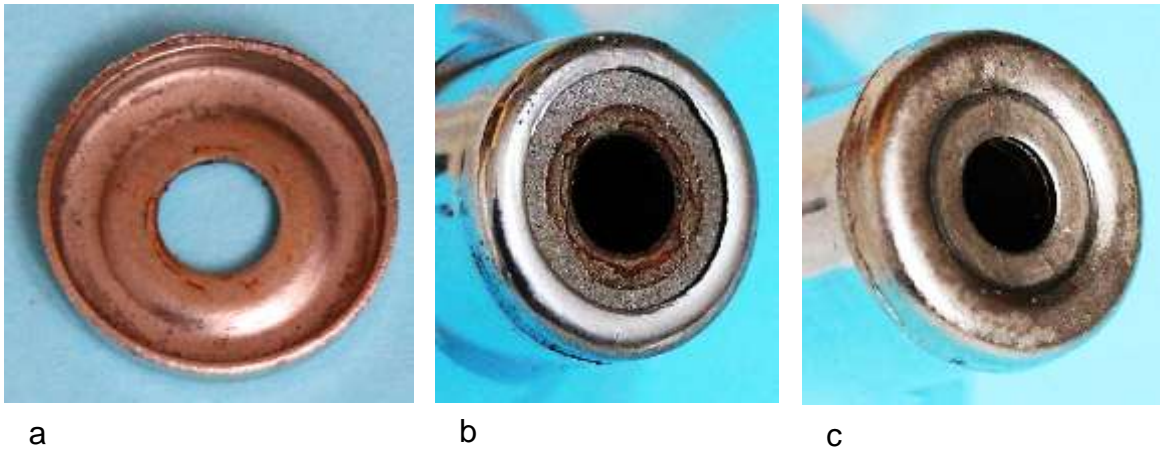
Obere Stirnseite des Lagers: a) Deckkappe. b) Umgebörtelter Lagerhalsrand, c) Aufgedrüsste Schutzkappe
